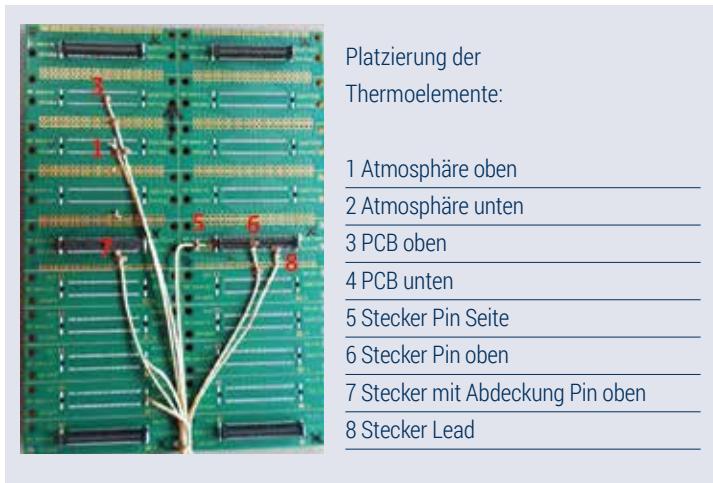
Steckverbinder-Testboard mit Thermoelementen
